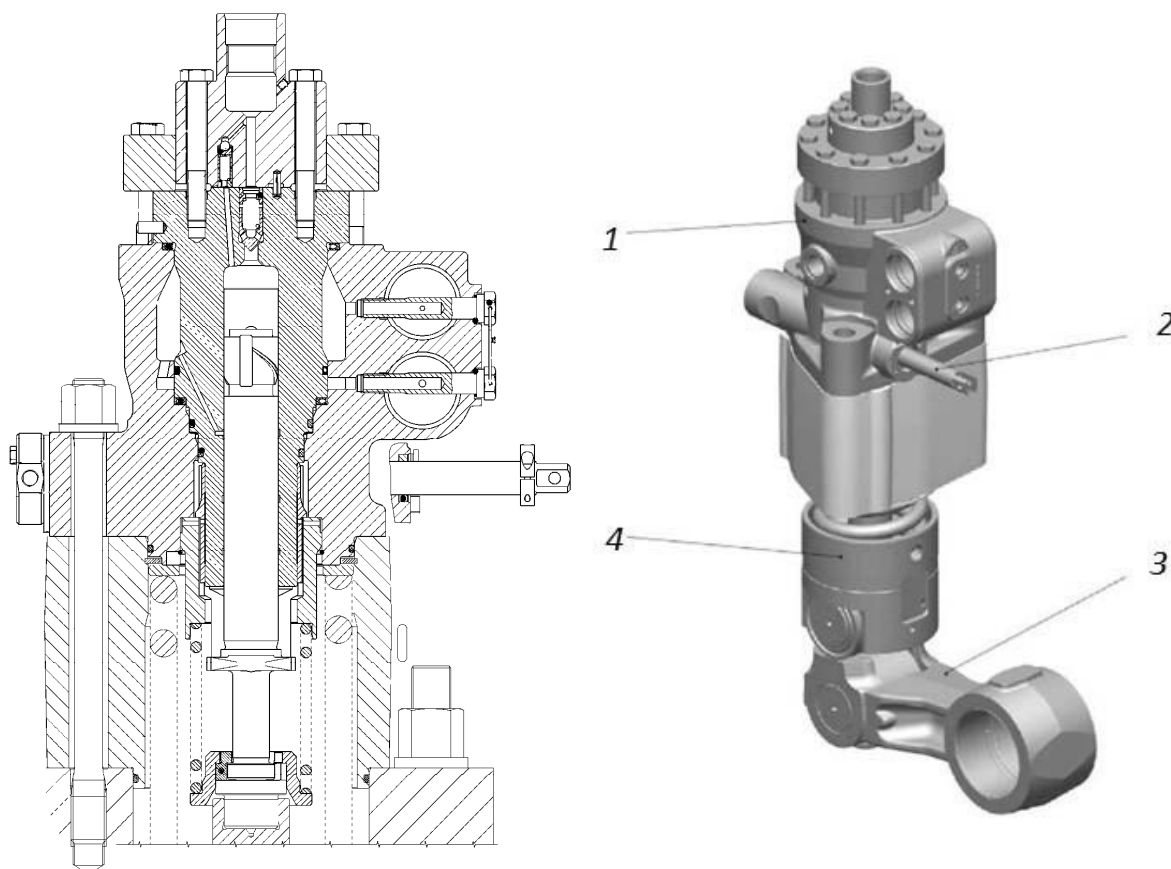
Паливний насос: 1 – плунжер; 2 – клерувальний шток; 3 – кулачковий механізм; 4 – роликовий штовхач
